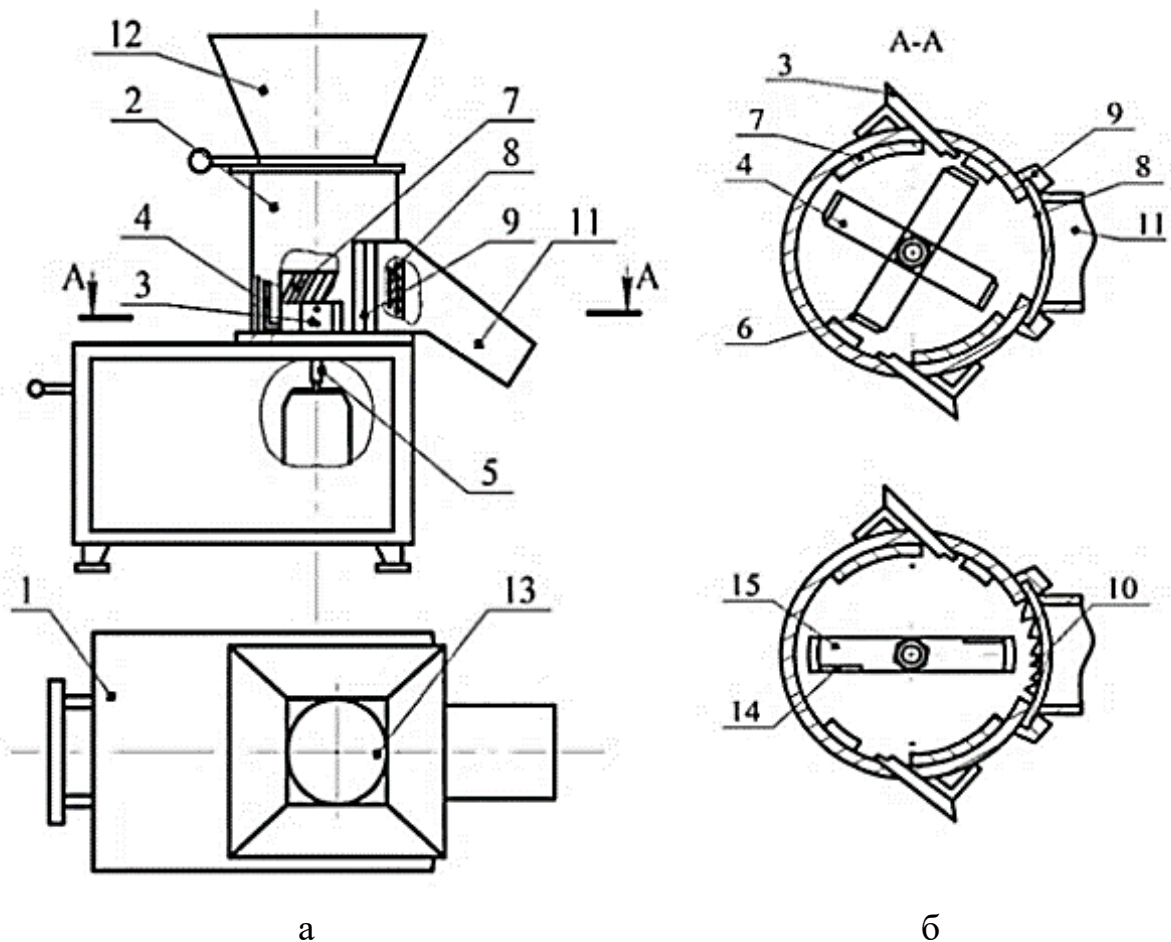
Універсальний подрібнювач кормів: а – загальний вигляд, б – вид А-А: 1 - основа; 2 – дробильна камера; 3 – бічні ножі; 4 - хрестоподібний ніж; 5 – вал; 7 – знімні накладки; 8 – змінні решета; 9 - напрямні; 10 - шатківниця; 11 - знімний рукав; 12 - знімний бункер; 13 – шибер; 14 знімний ніж; 15 – додаткові вертикальні ребра
